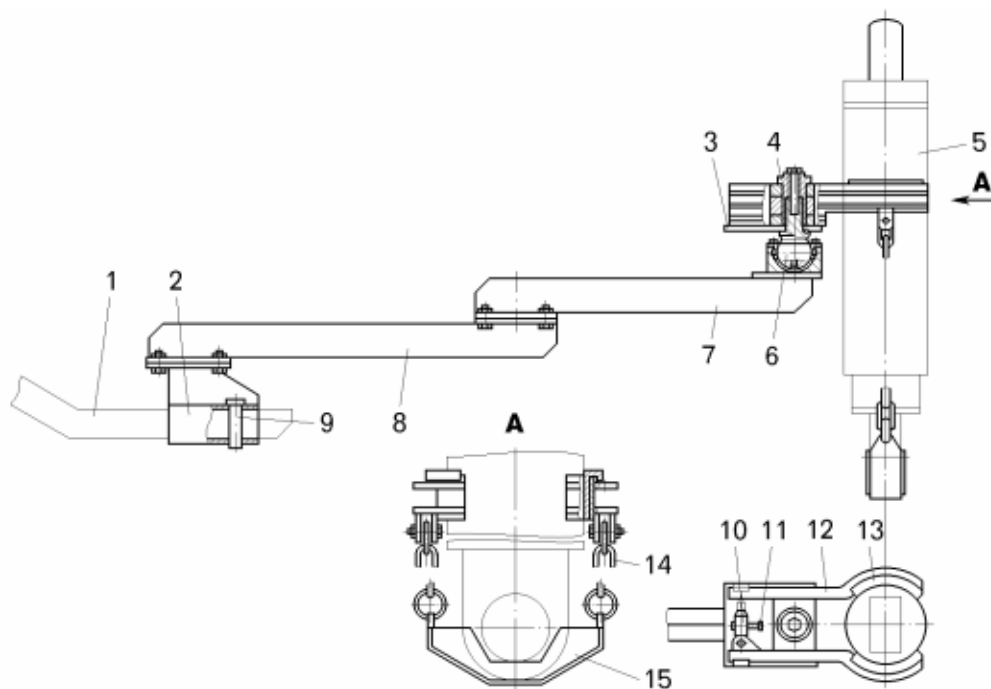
Приспособление для снятия цилиндров опрокидывающего механизма:
